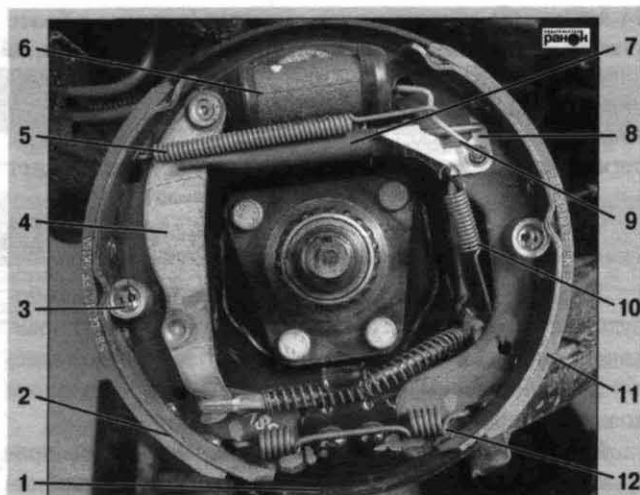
Тормозной механизм заднего колеса: 1 – тормозной щит; 2 – задняя колодка; 3 – опорная стойка; 4 – разжимной рычаг колодок; 5 – верхняя стяжная пружина; 6 – колесный тормозной цилиндр; 7 – распорная планка; 8 – рычаг регулятора; 9 – серьга; 10 – пружина рычага регулятора; 11 – передняя колодка; 12 – нижняя стяжная пружина; 13 – трос привода стояночного тормоза («ручника»).
